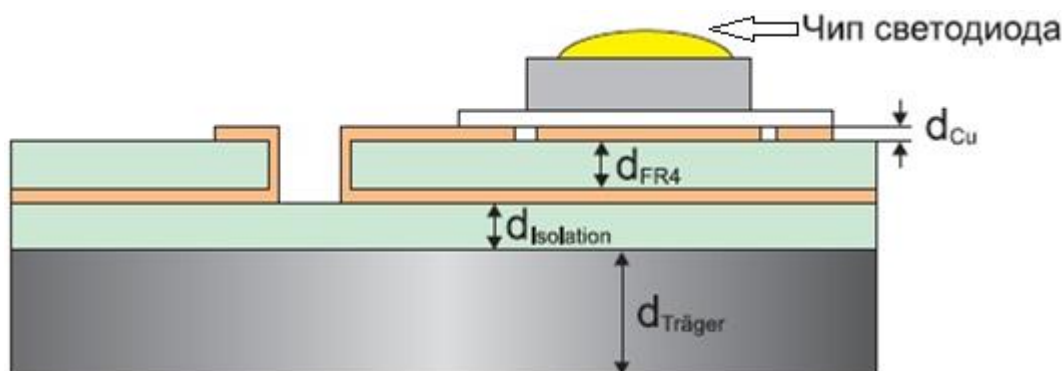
Схема конструкции платы с металлической подложкой [18]
